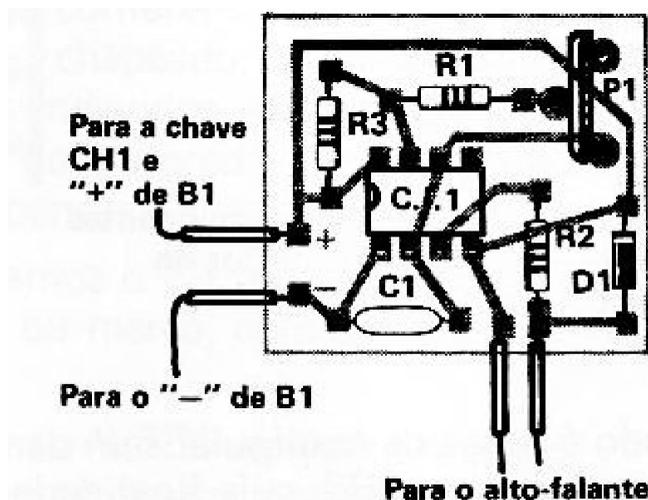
'Layout' dos componentes na placa construída artesanalmente.
